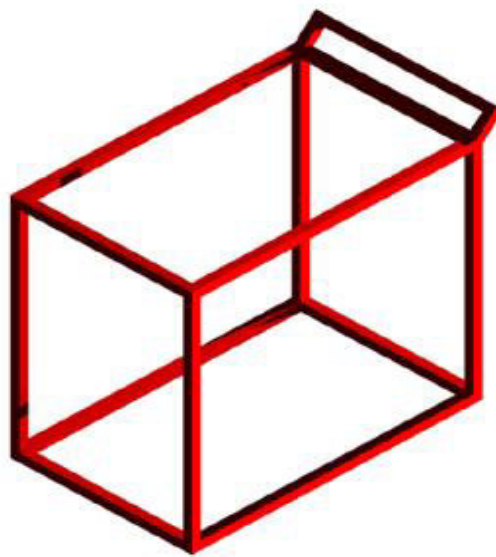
Estructura soporte, Juan Proaño (2010)
